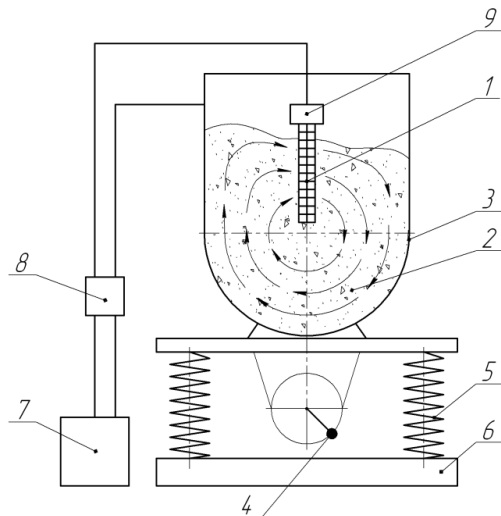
Схема электрофизической виброобработки: 1 – обрабатываемая деталь; 2 – рабочая среда; 3 – резервуар; 4 – вибровозбудитель; 5 – упругая подвеска; 6 – основание; 7 – трансформатор; 8 – прерыватель; 9 – держатель
